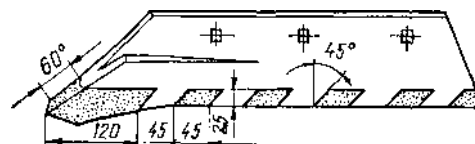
Леміш з ділянками, наплавленими твердим сплавом.
